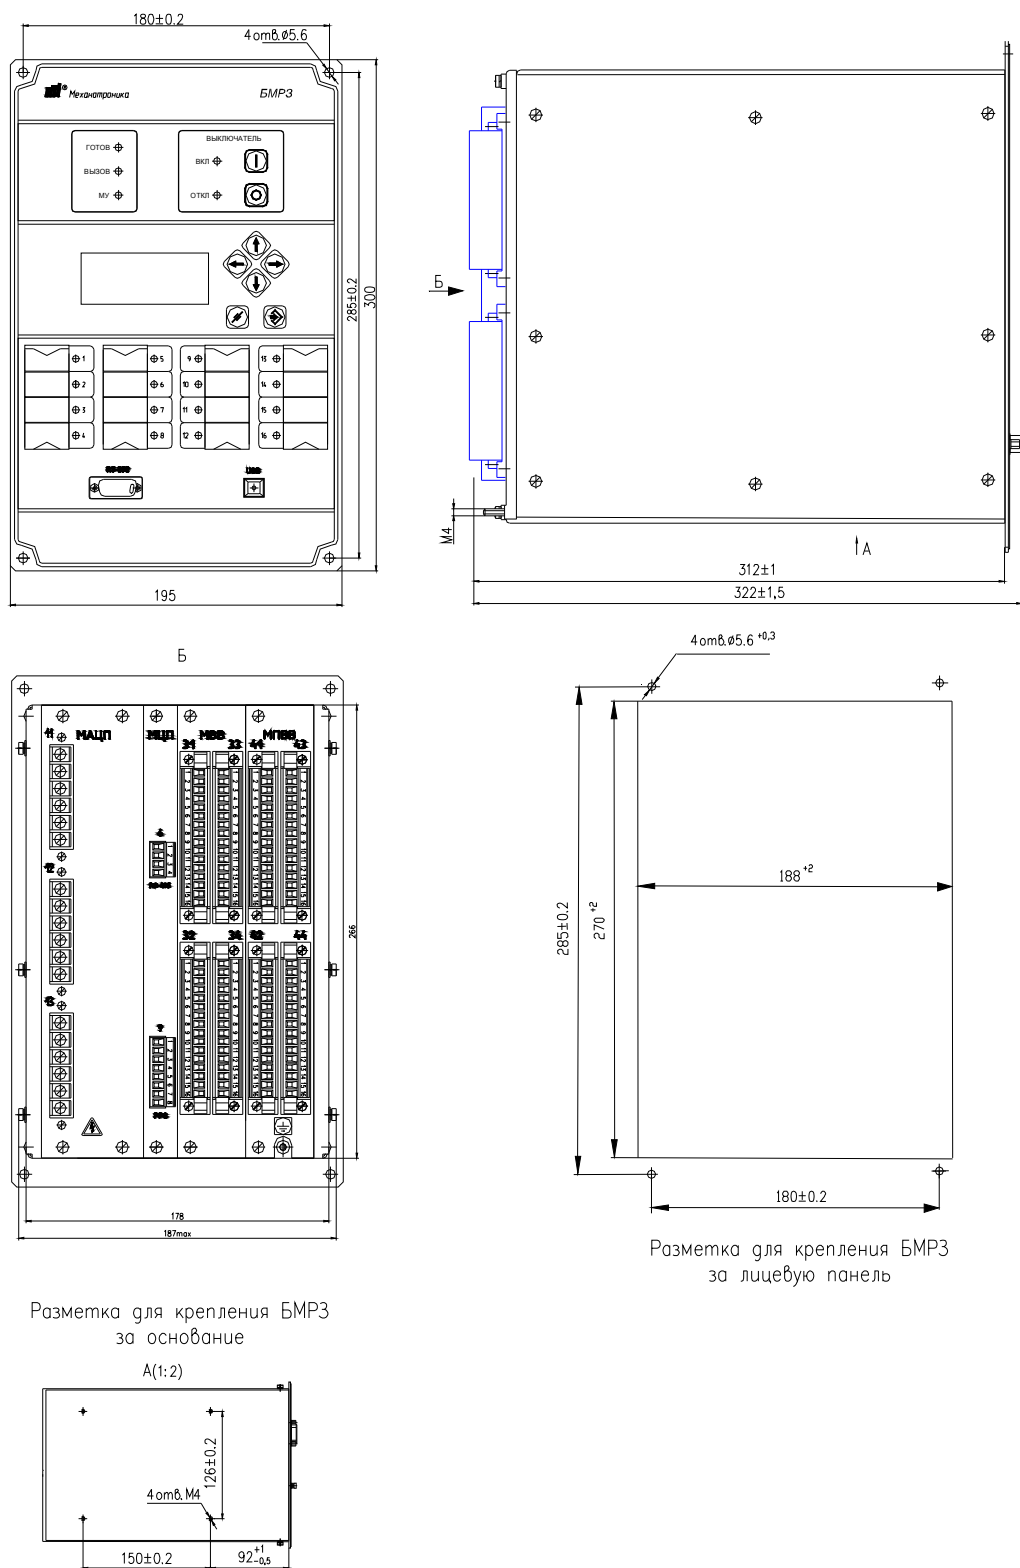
(лист 2 из 3) б - Габаритные, присоединительные и установочные размеры для BMP3 ДИВГ.648228.070
